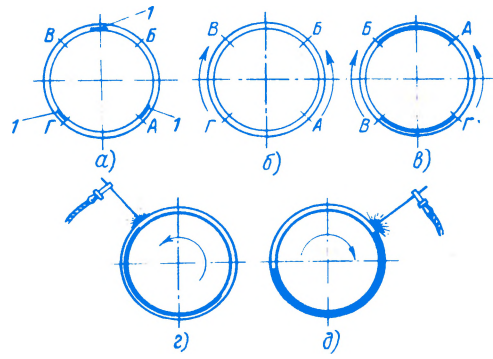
Порядок сварки стыков труб с поворотом:
